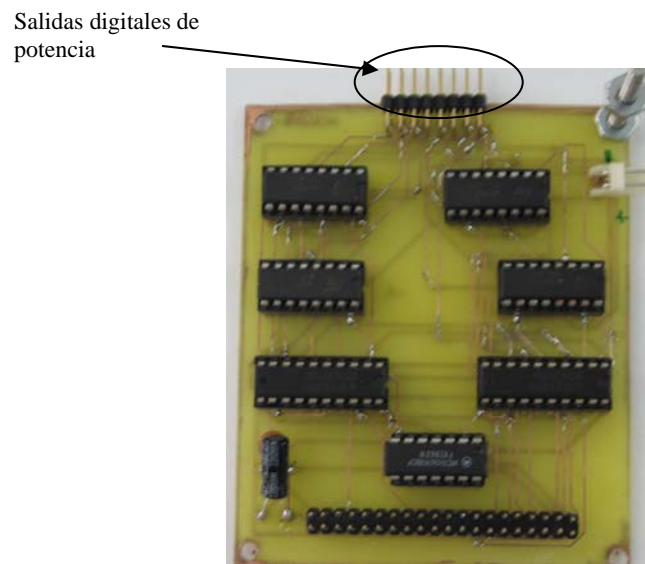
Ensamble físico de la cuarta parte de la tarjeta de control.
